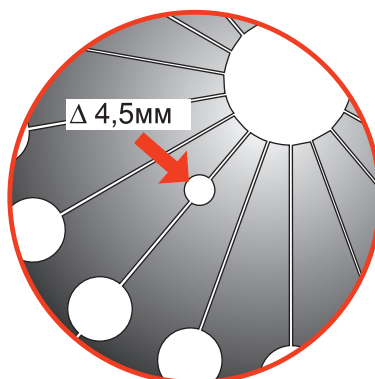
Лепестки нажимной пружины сцепления двигателя ВАЗ-2112.
